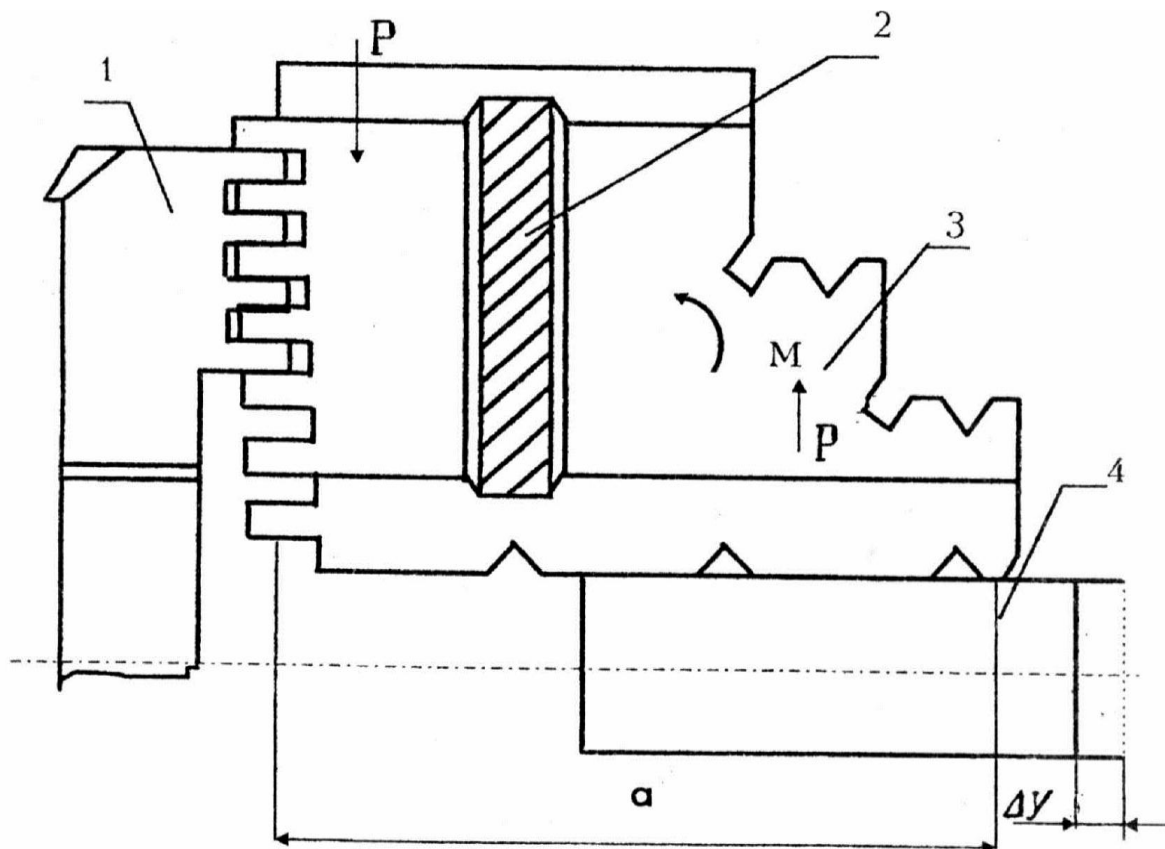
Схема закріплення заготовки у токарному патроні
